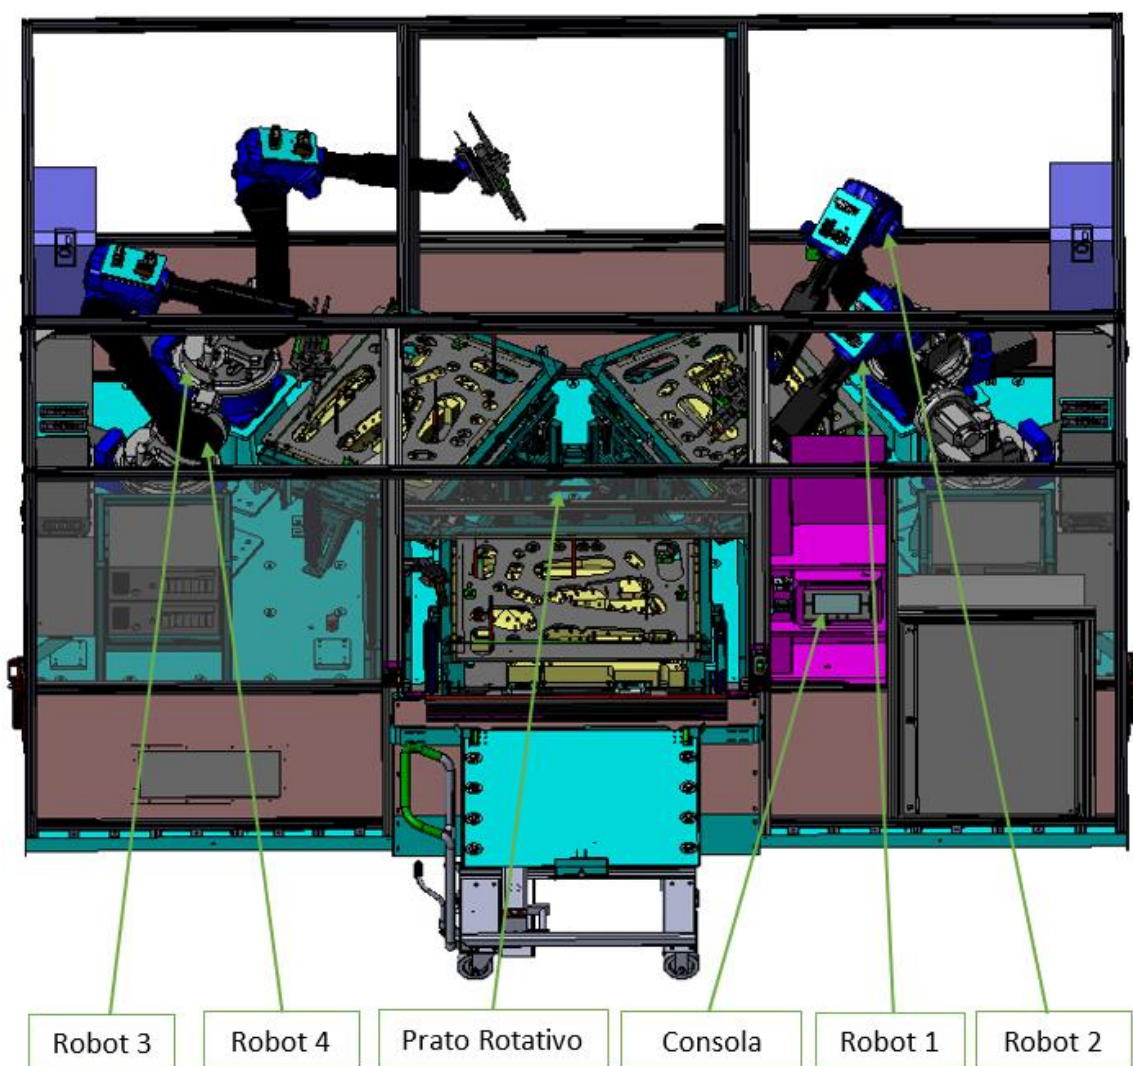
Célula de soldadura com 4 robôs [documentação interna].
